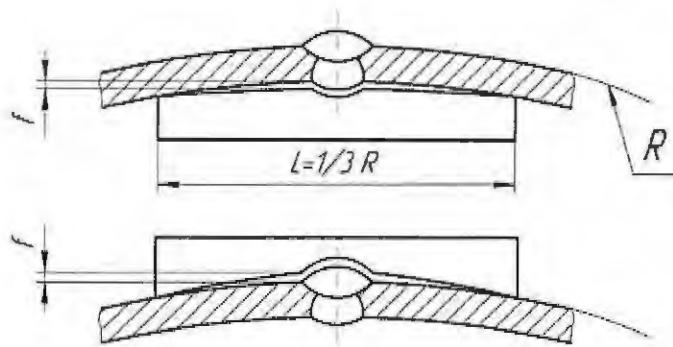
Схема замера угловатости сварного шва и отклонения формы детали от теоретической окружности в околосшовной зоне.
